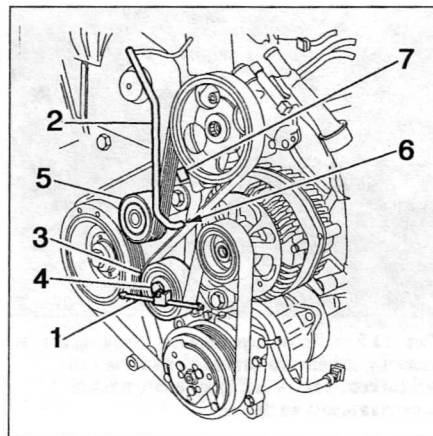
Ремень привода вспомогательных агрегатов и натяжитель (двигатели серии DW с кондиционером)
